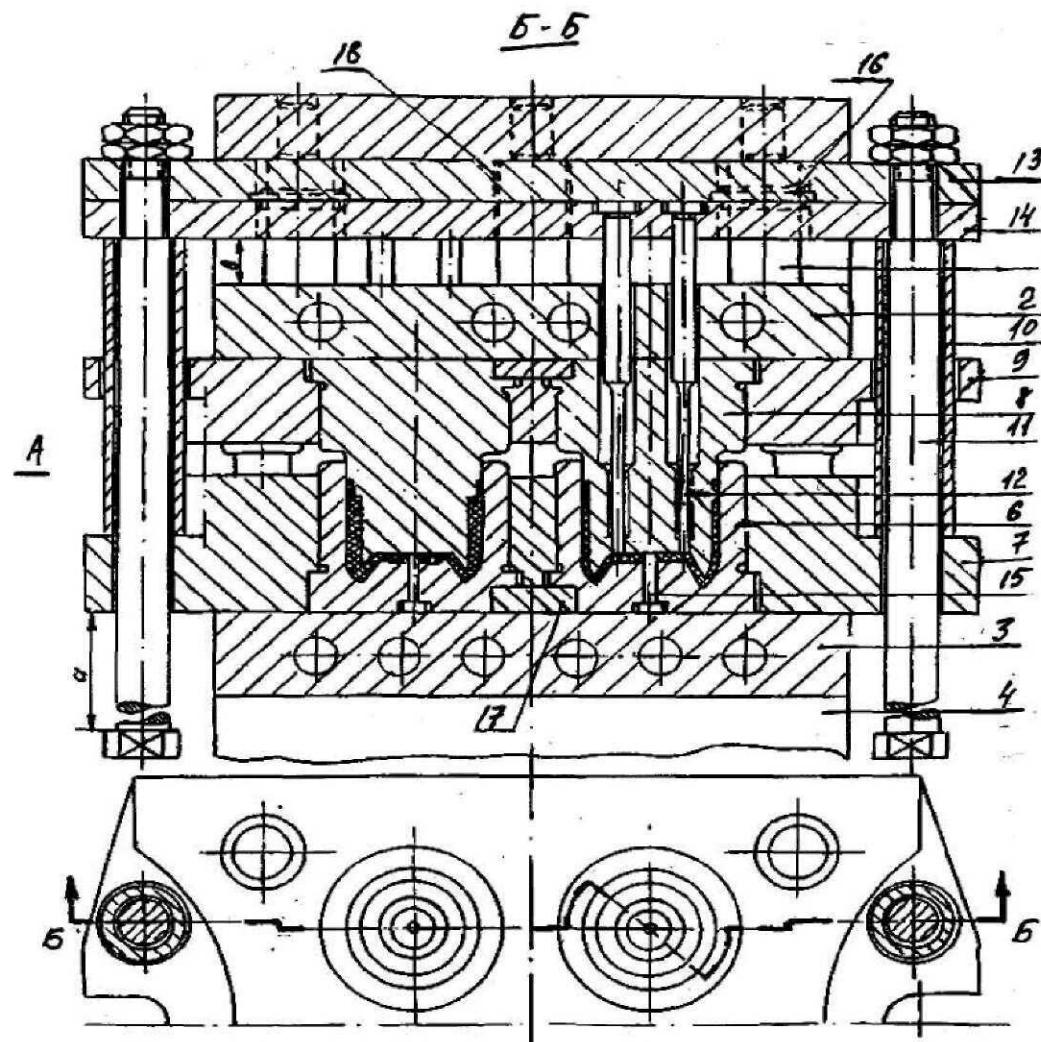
Пресс-форма для изготовления крышки футляра:
